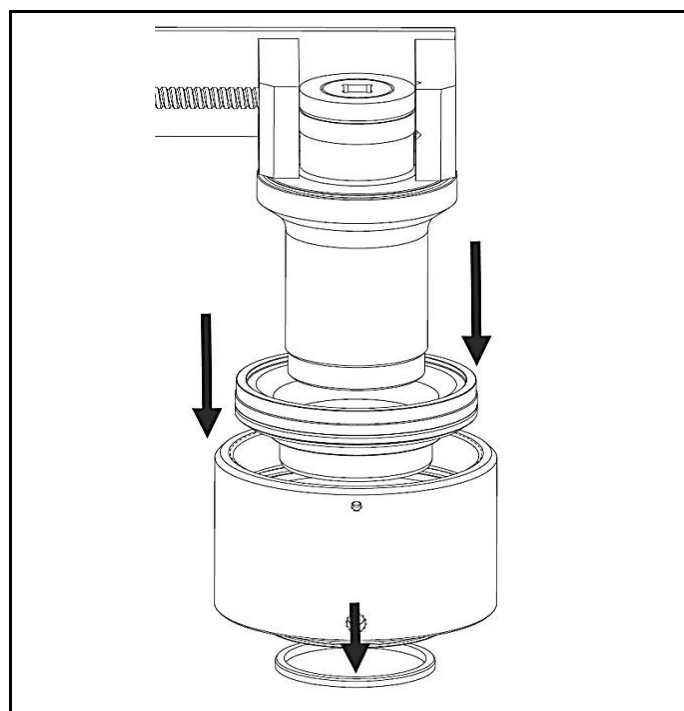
Körper, Lagerring, Einsatzbaugruppe ausbauen.
